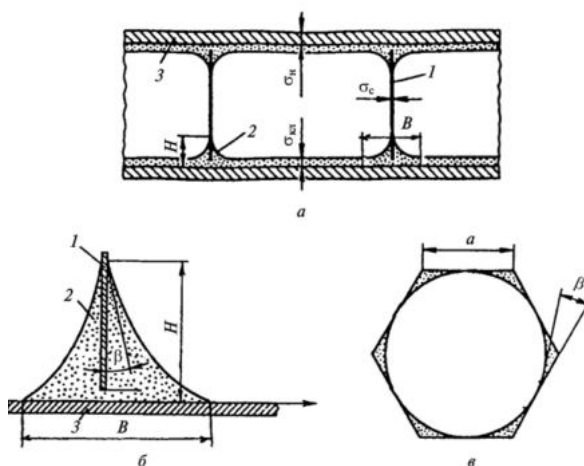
Сечения сотовой ячейки (а,в) и клеевой галтели(б): 1— стенка сотового заполнителя; 2— галтель; 3— обшивка
